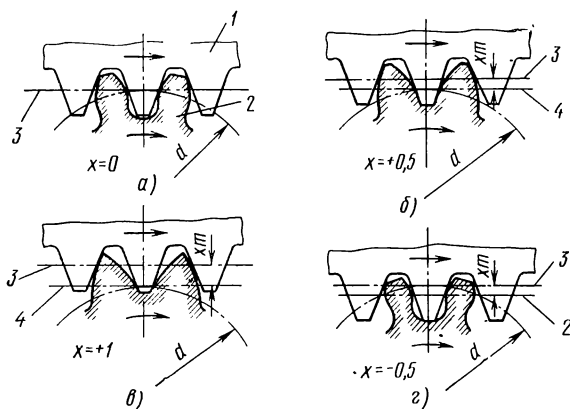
Влияние смещения инструментальной рейки на форму эвольвентного профиля зуба
